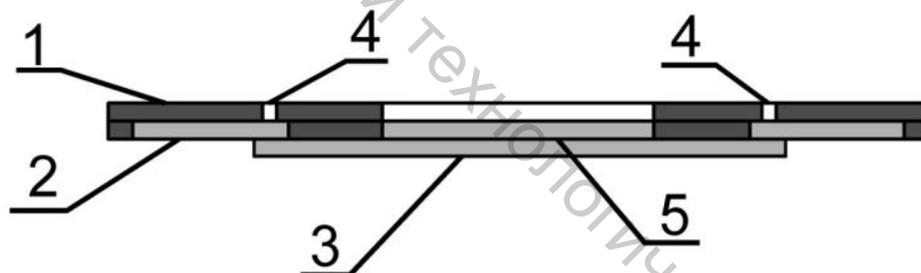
Порядок размещения деталей верха обуви в кассете: 1 – верхняя пластина, 2, 5 – настрочные детали, 3 – основная деталь
